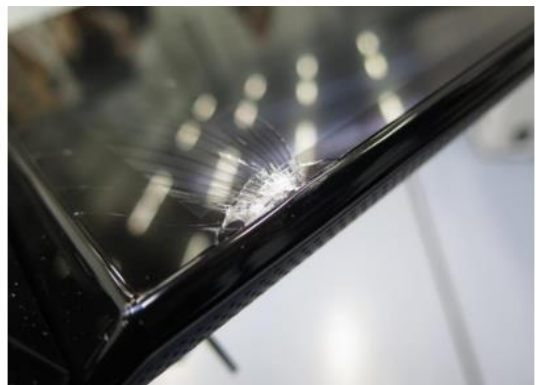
Obr. I Přístrojová deska před zkouškou číslo 1 – zdroj autor
